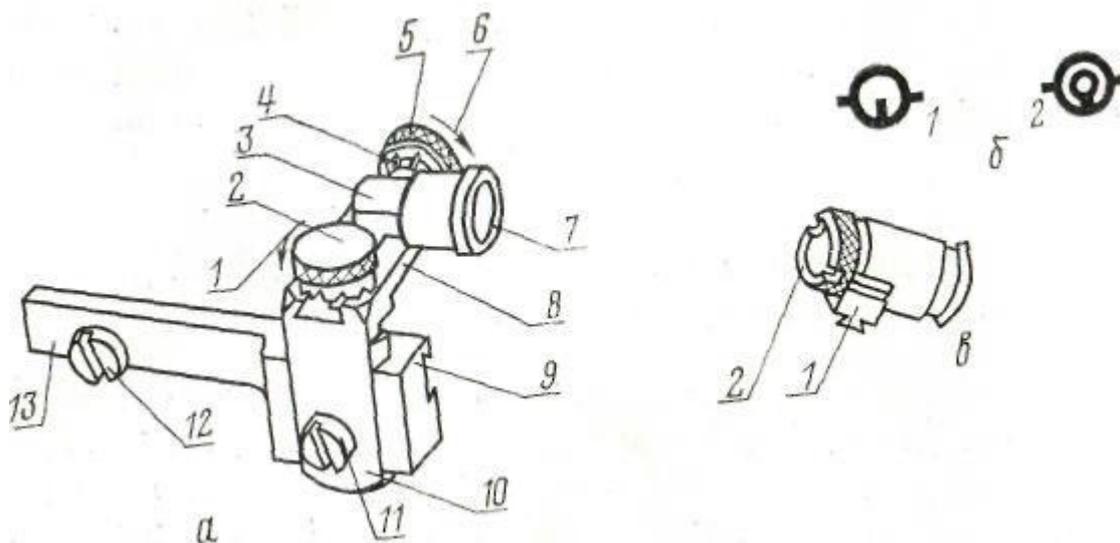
Прицельные приспособления винтовки ТОЗ-12:
